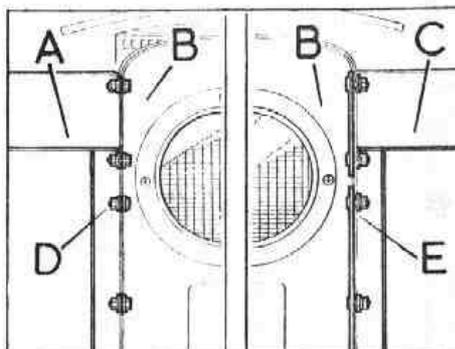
Elementos de fijación de la calandra a las aletas
